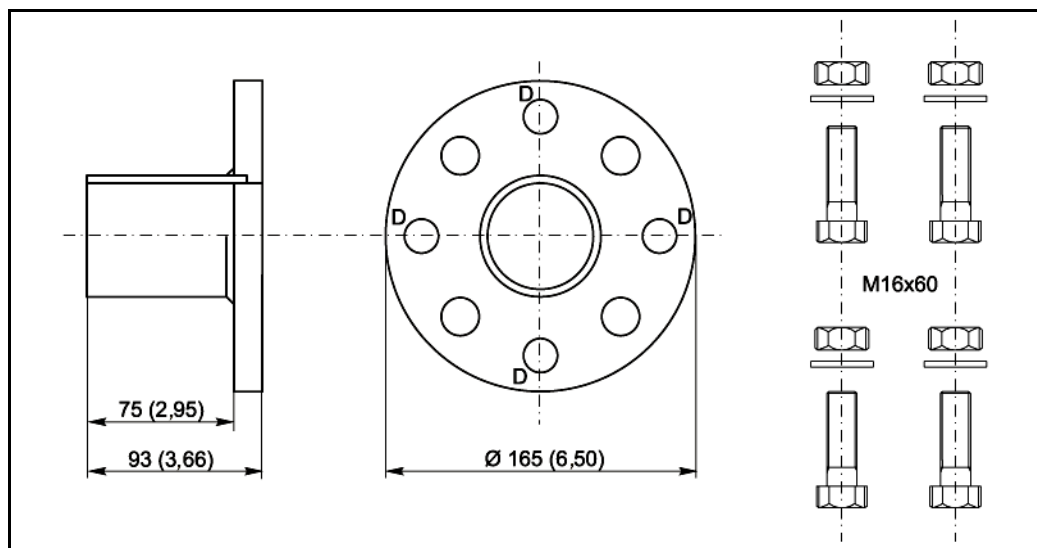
Сварная муфта, размеры в мм (дюймах)
